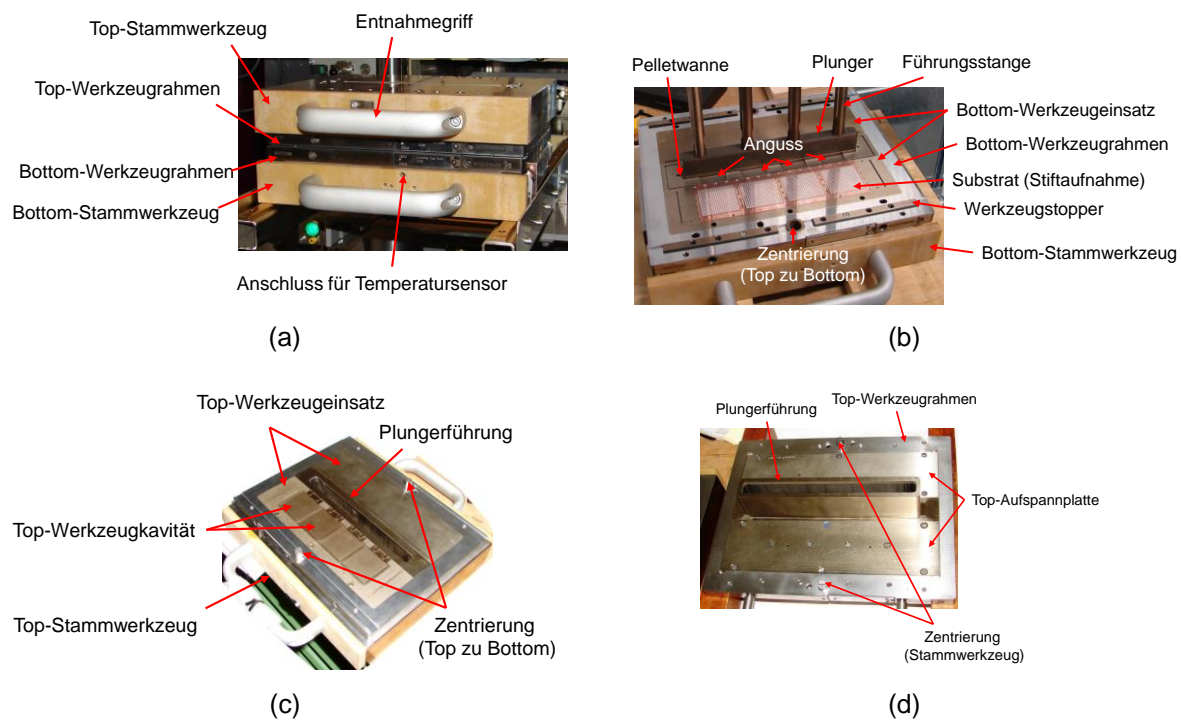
Beschriftete Darstellung von (a) dem zusammengebauten Werkzeug bestehend aus Stammwerkzeug und Werkzeugrahmen, (b) der Detailansicht des auf dem Bottom-Stammwerkzeug montierten Bottom-Werkzeugrahmens, (c) der Detailansicht des auf dem Top-Stammwerkzeug montierten Top-Werkzeugrahmens und (d) der Rückansicht des Top-Werkzeugrahmens.
